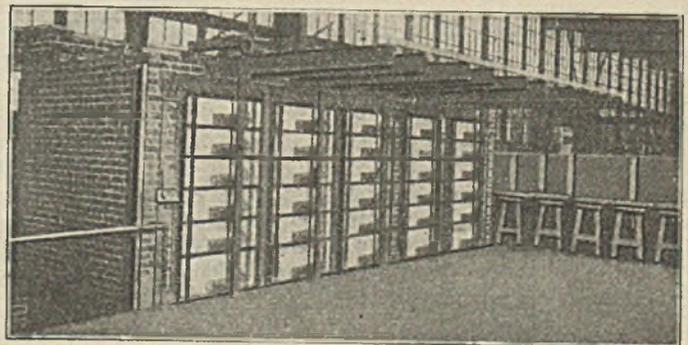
Ansicht der Kerntrockenöfen der Gießerei der Universal Winding Co.
